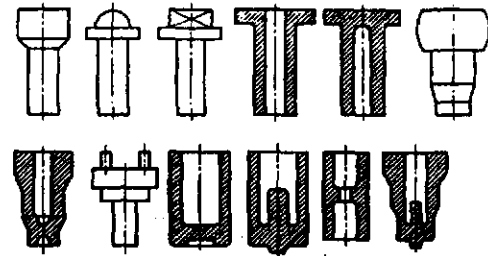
Типовые заготовки деталей, получаемые холодной объемной штамповкой выдавливанием
